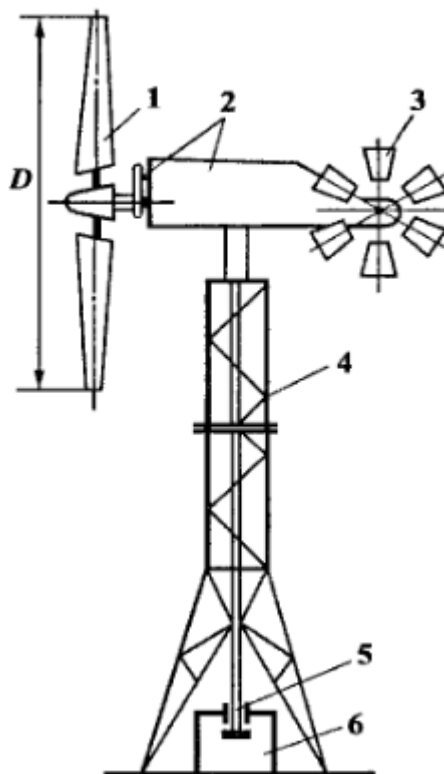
Конструктивна схема ВЕУ з горизонтальною віссю обертання: 1- робоча лопасть; 2- трансмісія (мультиплікатор); 3- віндроза; 4 – вишка; 5- вал відбора потужності; 6- електрогенератор.
